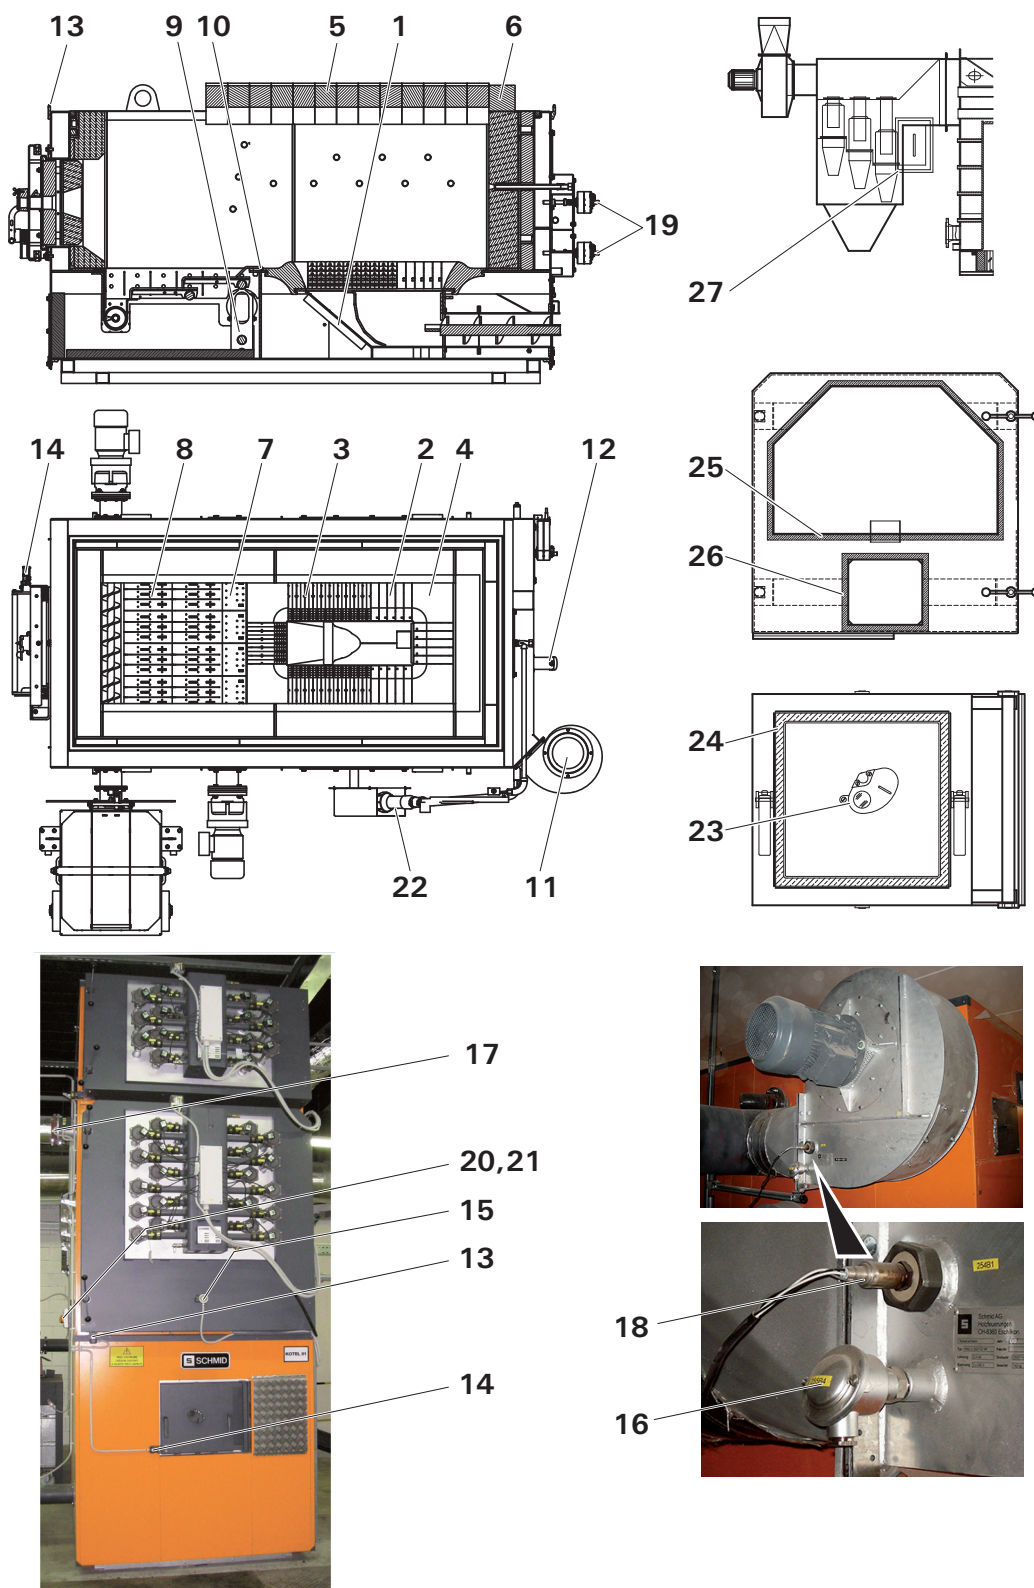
Pièces de rechange chaudière à grille mobile UTSP
